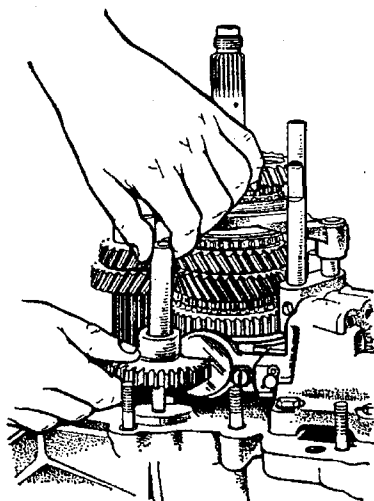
Снятие и установка оси и промежуточной шестерни заднего хода
